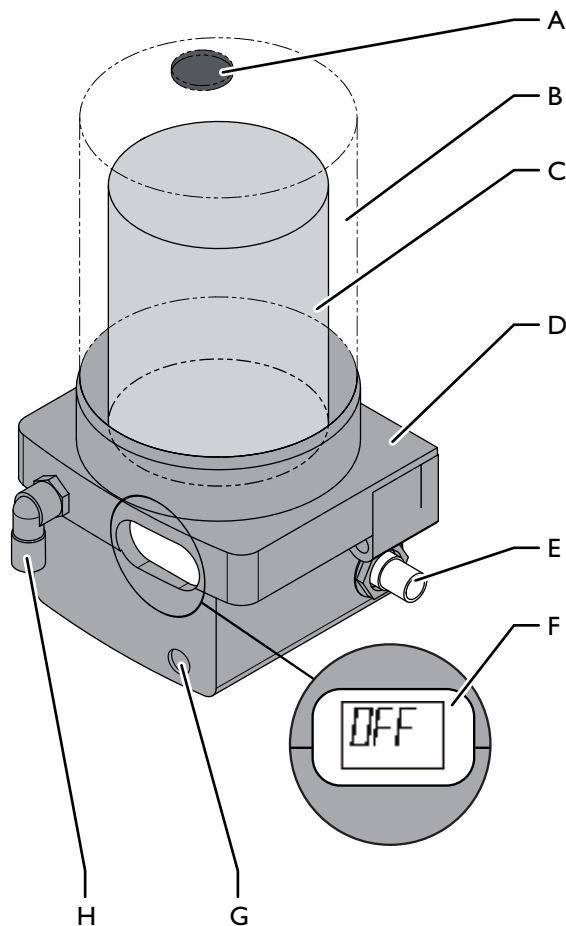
Детальная конструкция FlexxPump 401 mod
